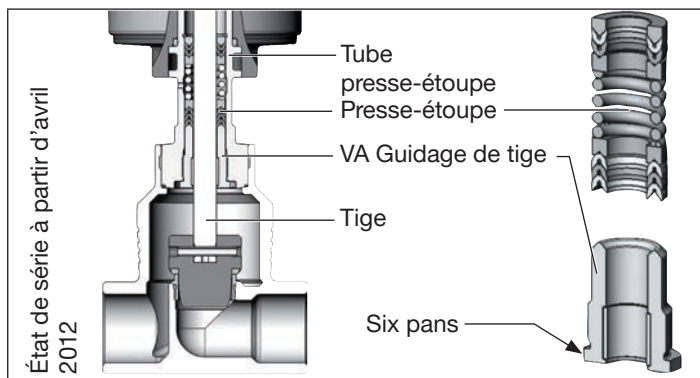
Remplacement du presse-étoupe (VA guidage de tige)
